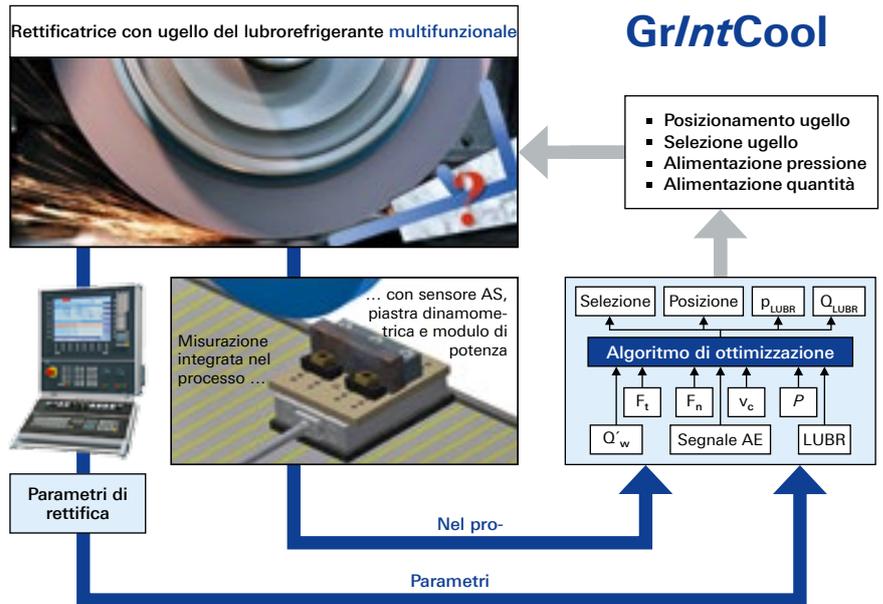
Panoramica del progetto "GrintCool - Grinding with intelligent coolant supply"
